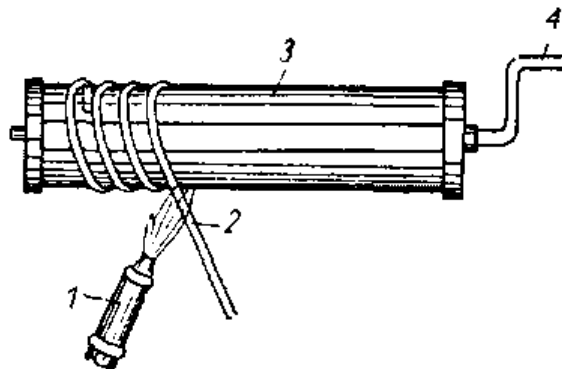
Изготовление спирали из стеклянной трубки: 1 — газовая горелка; 2 — стеклянная трубка; 3 — деревянный вал с клиньями; 4 — ручка для вращения.
